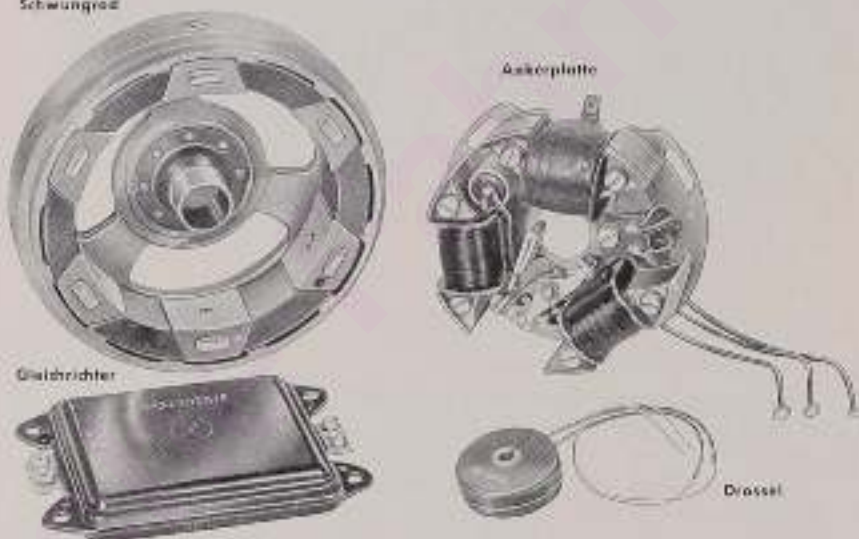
Bosch-Schwinglichtmagnetzündar LM-UTG 1/154/45 mit Gleichrichter und Drossel
